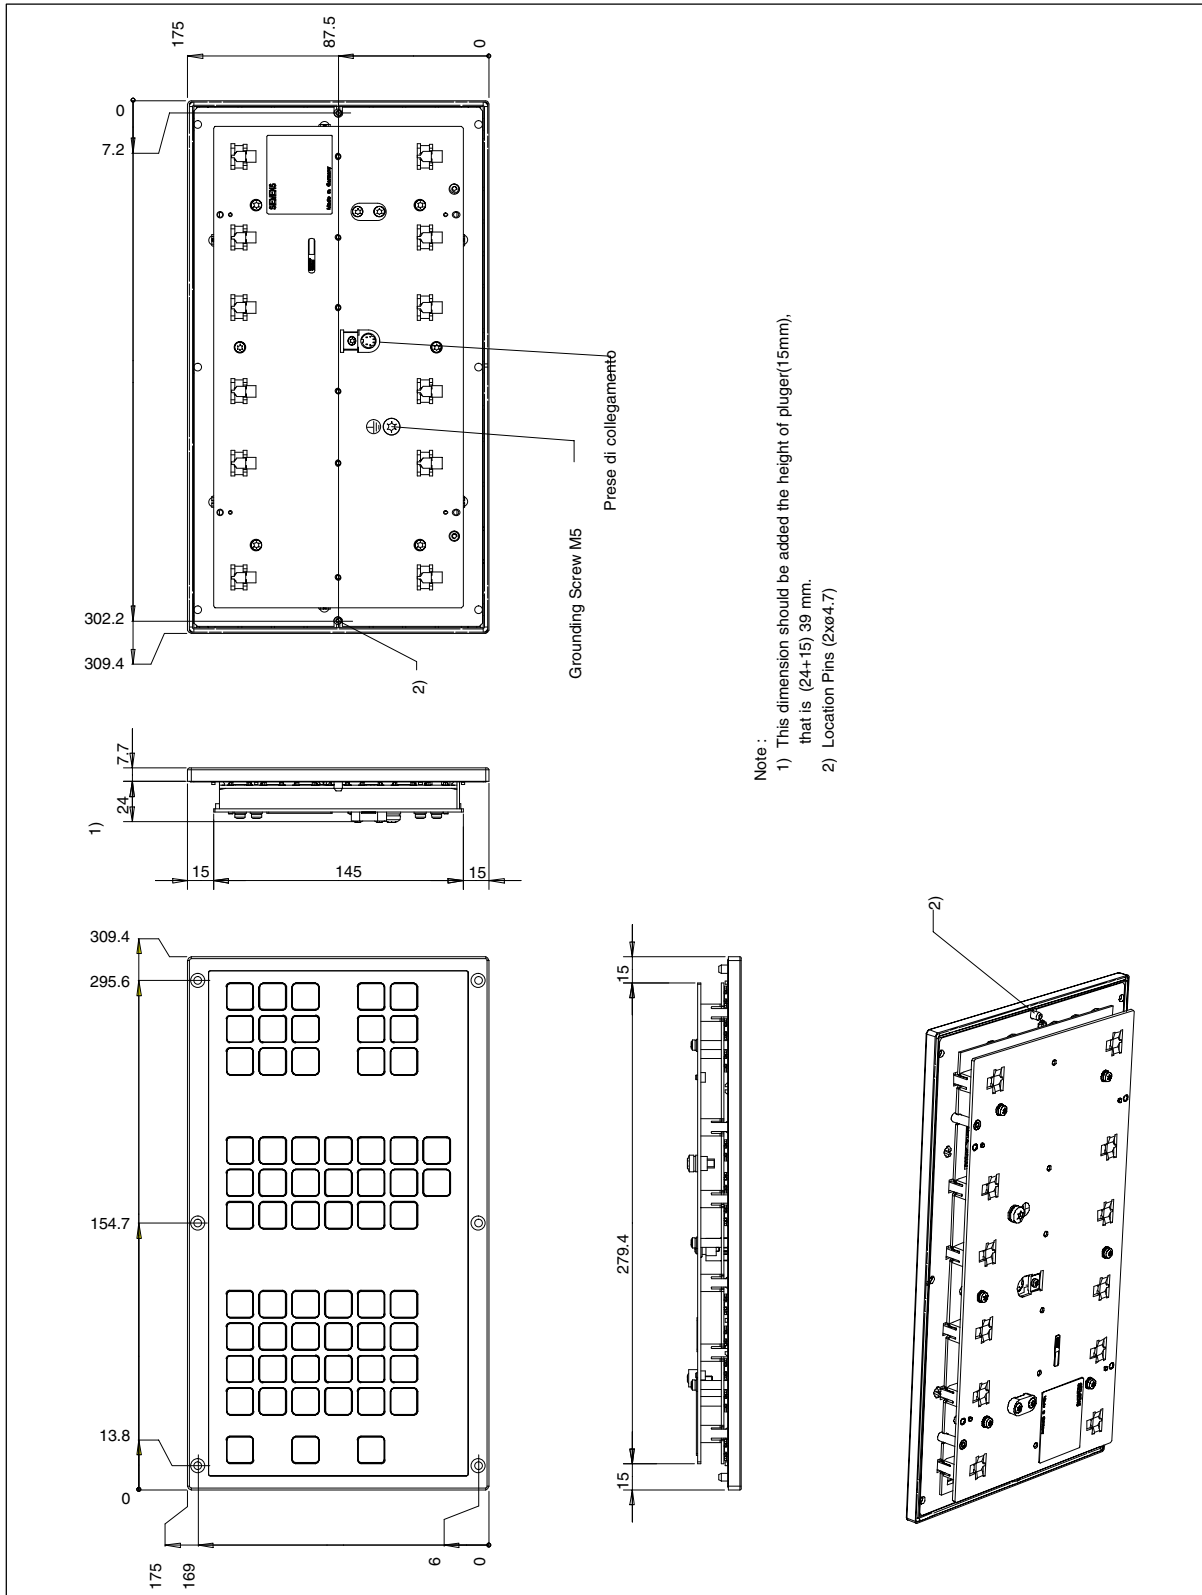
Dimensioni di ingombro Keyboard (layout orizzontale per il montaggio sotto alla PCU)
